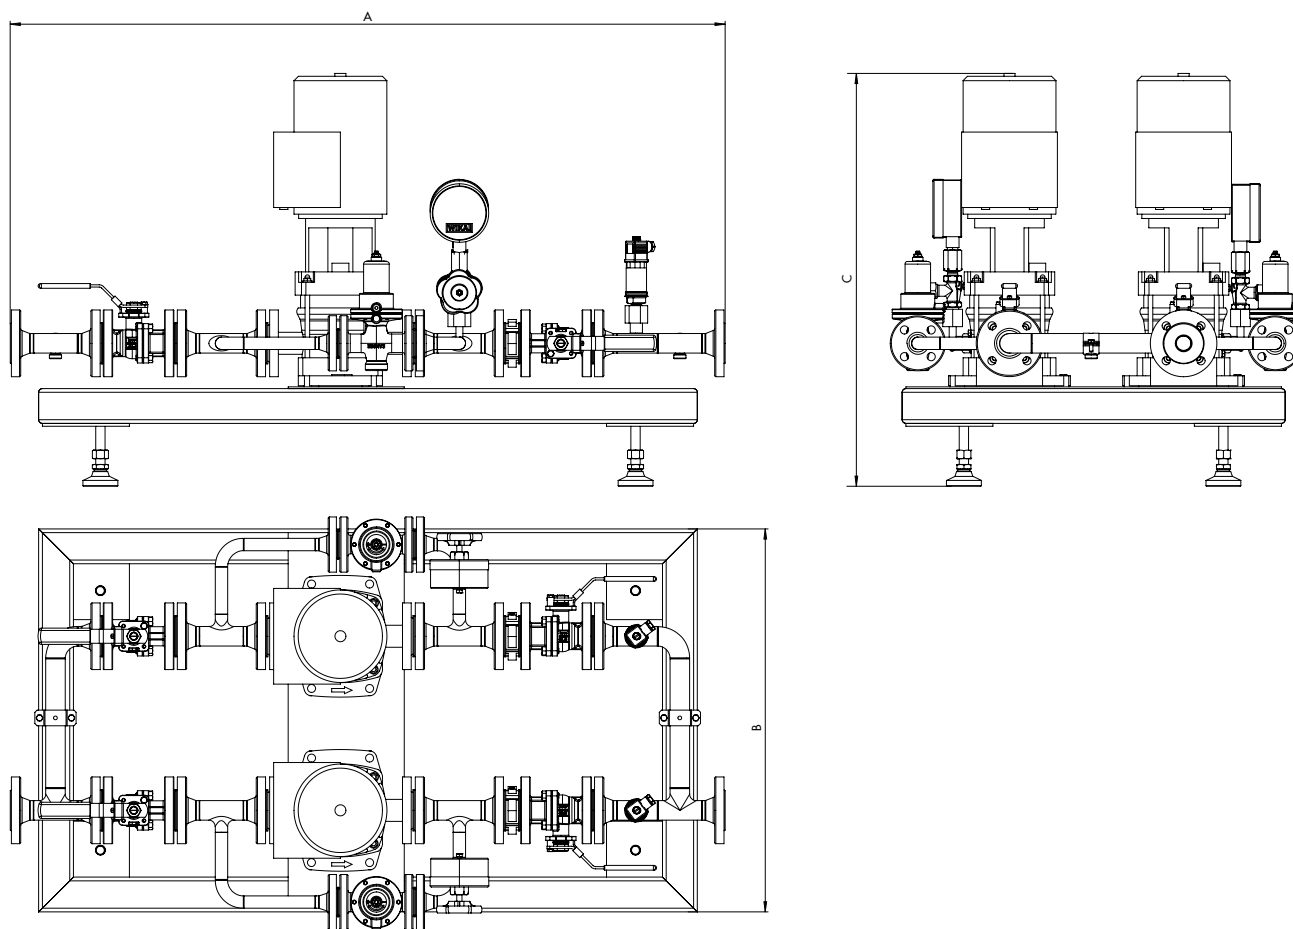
Abmessungen und Gewichte Pumpenbaugruppe Typ 7111-1/-2 · Schematische Darstellung
